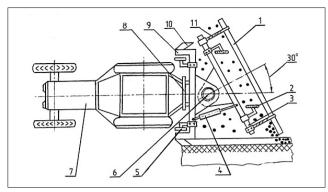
Принципиальная схема агрегата: 1 — гребенка; 2 — опорные колеса гребенки; 3 — подвижная рама; 4 — гидроцилиндр; 5 — опорные колеса плуга; 6 — поворотное устройство; 7 — трактор МТЗ-82; 8 — навесное устройство; 9 — неподвижная рама; 10 — корпус плуга; 11 — пружинные стойки Fig. 1. Schematic diagram of the machine: 1 — comb; 2 — support comb wheels; 3 — movable frame; 4 — hydraulic cylinder; 5 — support plow wheels; 6 — rotary device; 7 — MTZ-82 tractor; 8 — mounted device; 9 — fixed frame; 10 — plow body; 11 — spring struts
